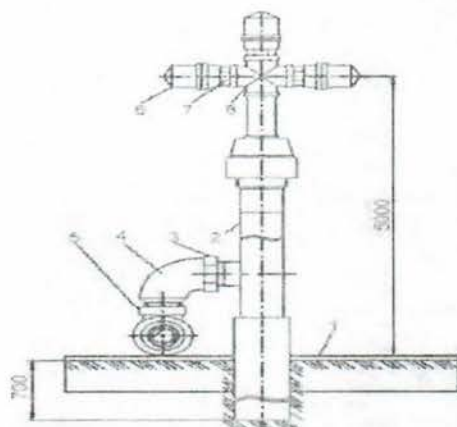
Дождеватель: 1 – основание (анкер); 2 – трубчатый стояк; 3 – контргайка; 4 – угольник; 5 – тройник; 6 – насадка; 7 – ниппель; 8 – крестовина
